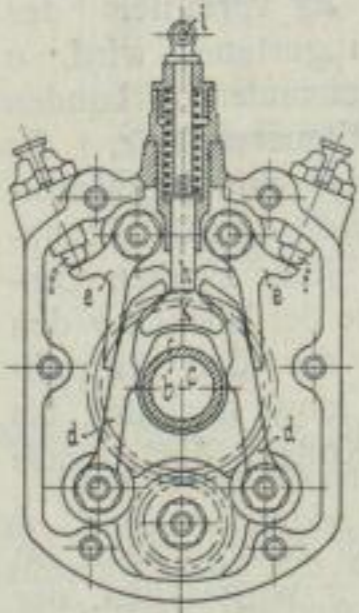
Steuerung für die Ventile beim Adler Zwei-zylindermotor.
